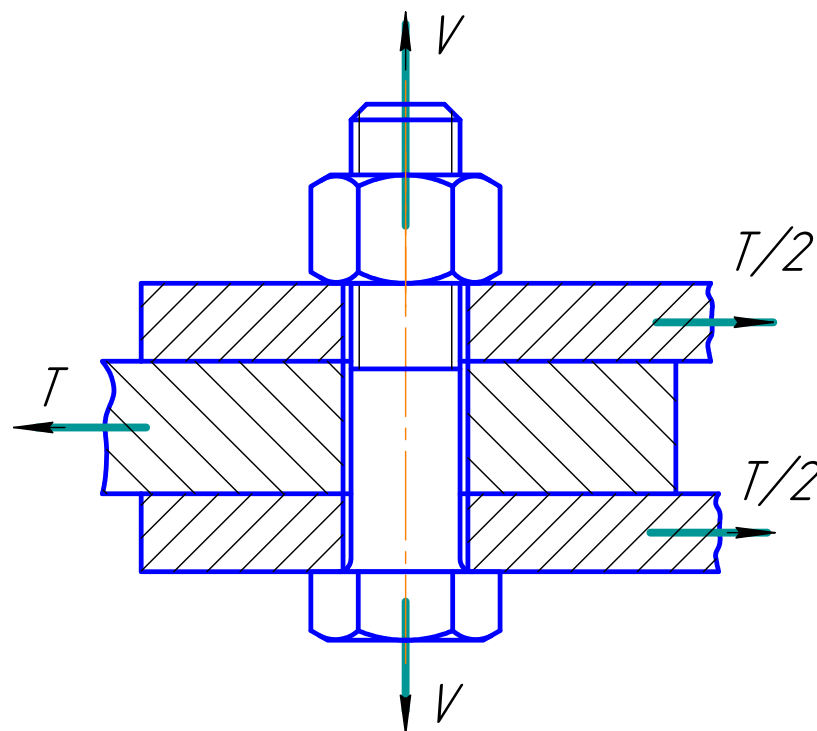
Схема для розрахунку болтового з'єднання, навантаженого поперечною силою
